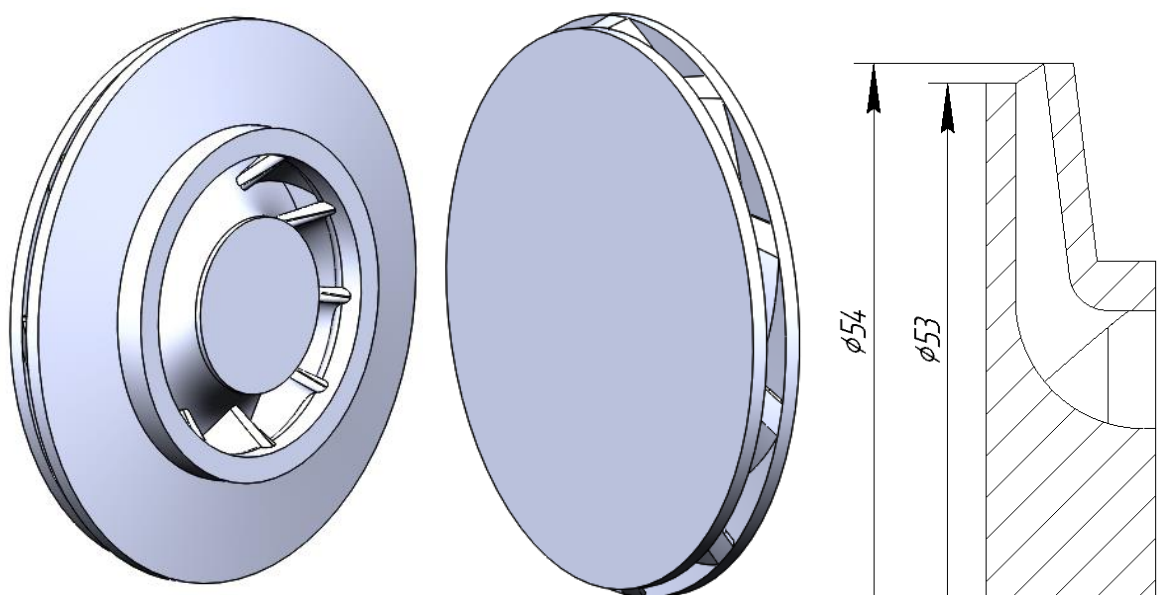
Рабочее колесо габарита 2А базового варианта
